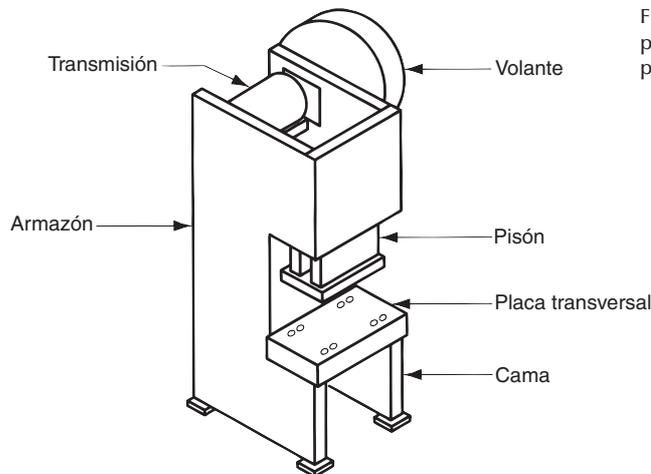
Componentes de una prensa troqueladora típica accionada por transmisión mecánica.
